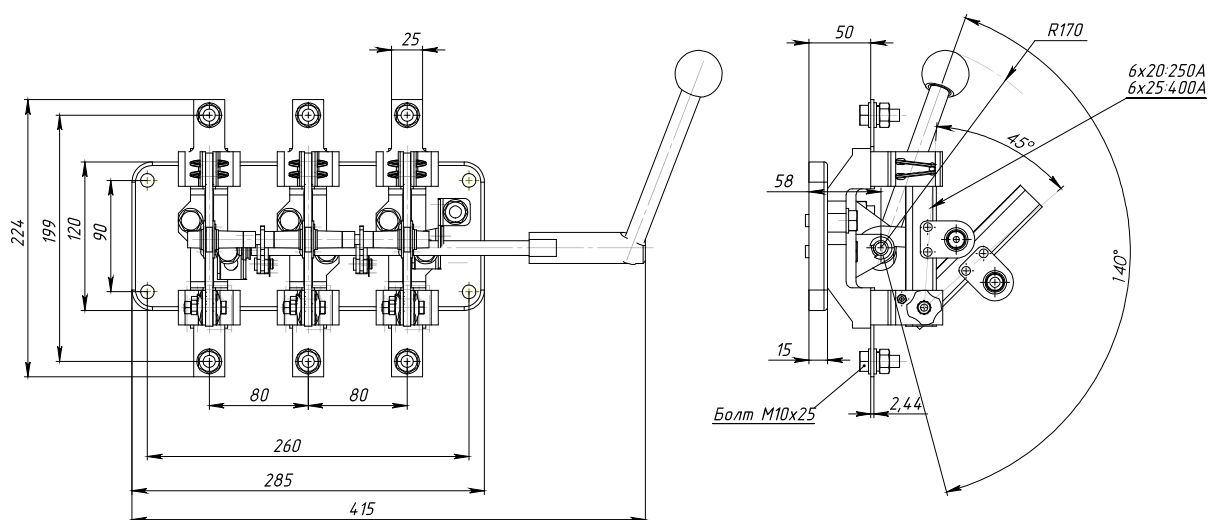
Разъединитель PE19-35(37)-31150-00 УХЛЗ с боковой смещенной рукояткой
